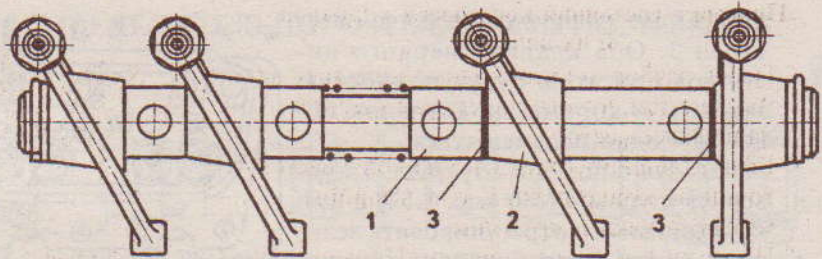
Установка дополнительных шайб для устранения осевого люфта коромысел: 1 - распорная втулка; 2 - коромысло; 3 - регулировочные шайбы
